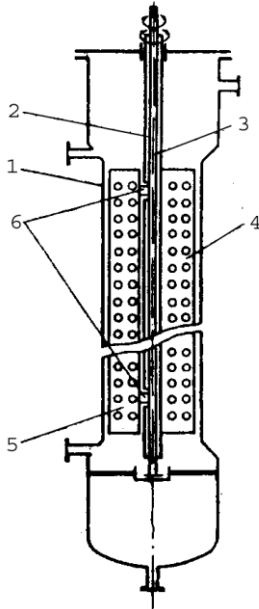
6. Аппарат с асинхронным движением насадки. 1- корпус; 2 – ротор; 3 –вал; 4, 5 – пластины; 6 - поводок
